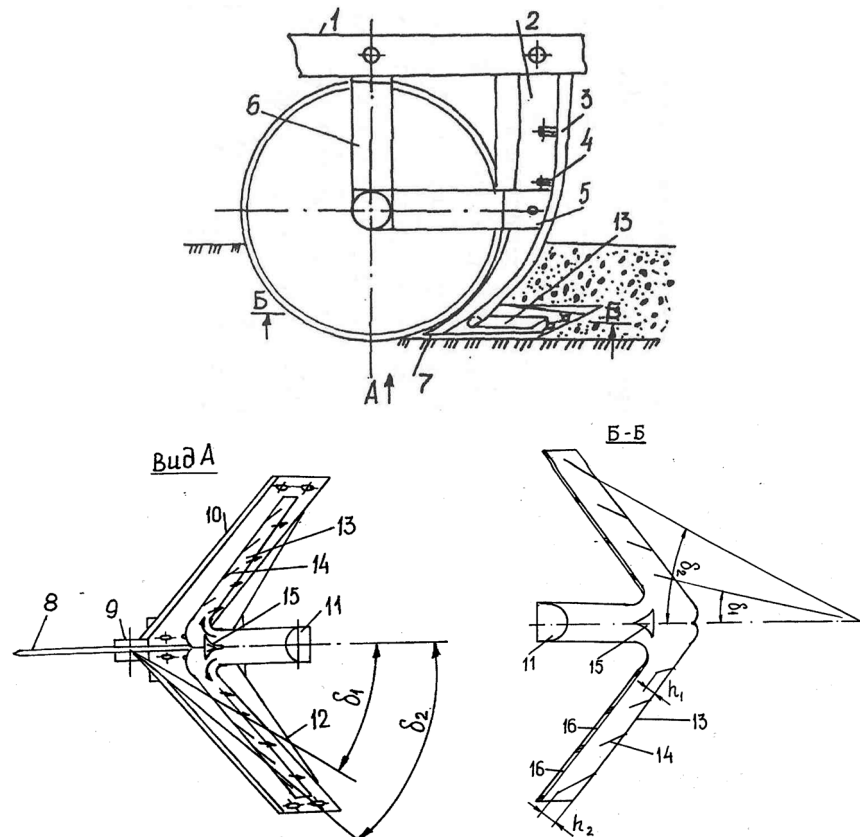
Комбинированный рабочий орган почвообрабатывающего орудия
